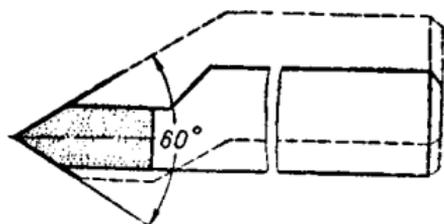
Сопоставление обычного резьбового резца с резьбовым резцом В. М. Бирюкова.
